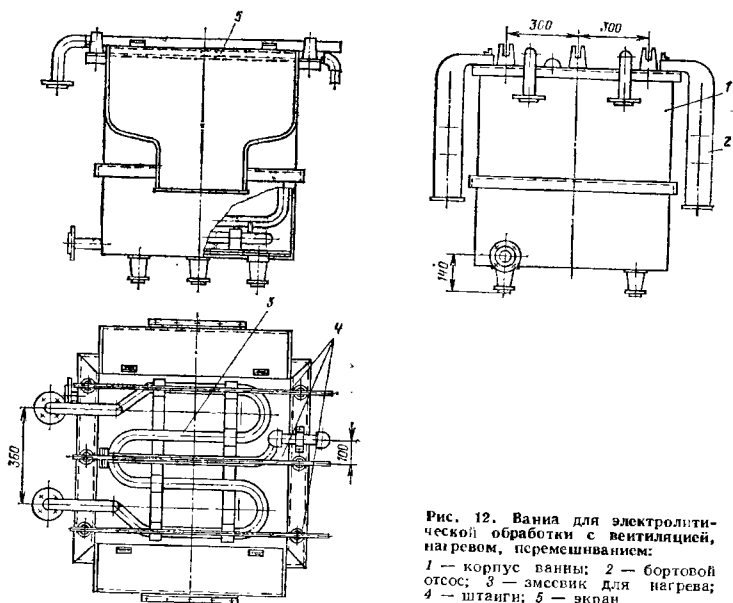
Ванна для электролитической обработки с вентиляцией, нагревом, перемешиванием:
